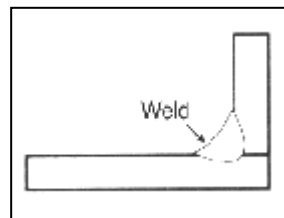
Esquina soldada desde adentro - pobre adentro, peor afuera
